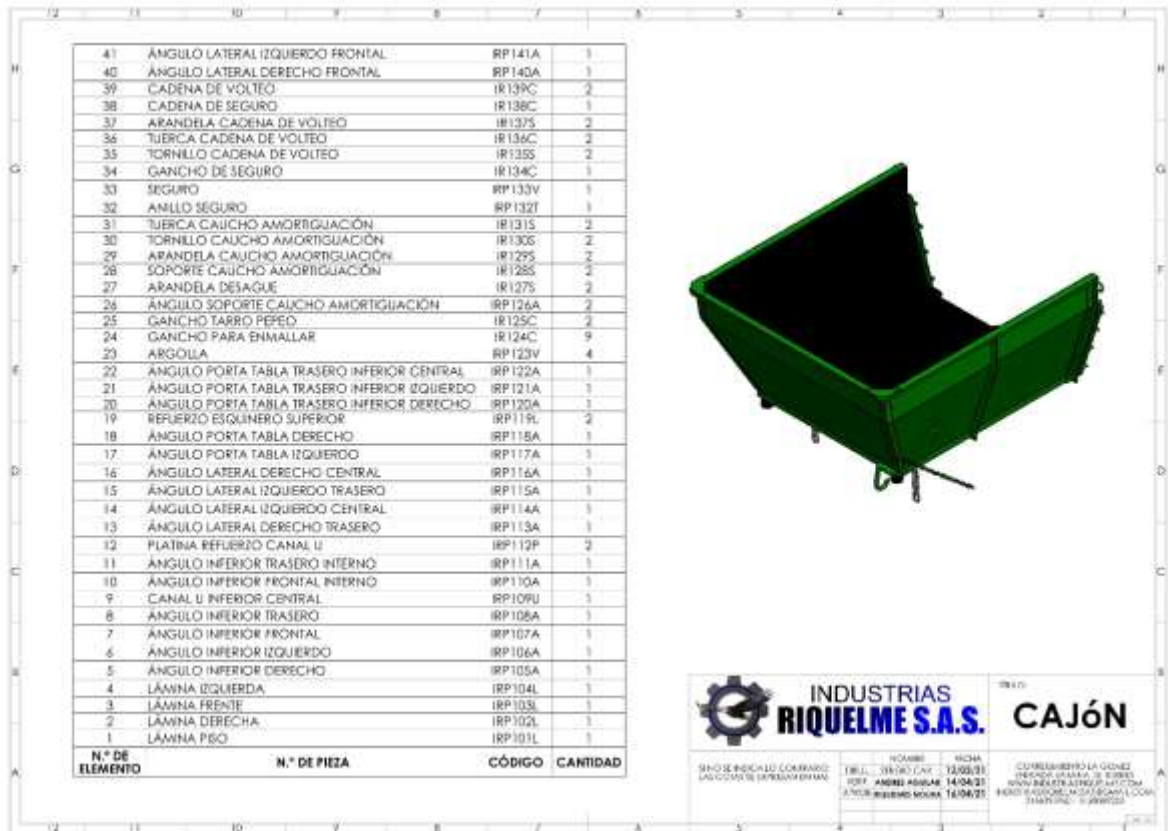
Plano mecánico remolque agrícola para búfalo vista isométrica explosionada
